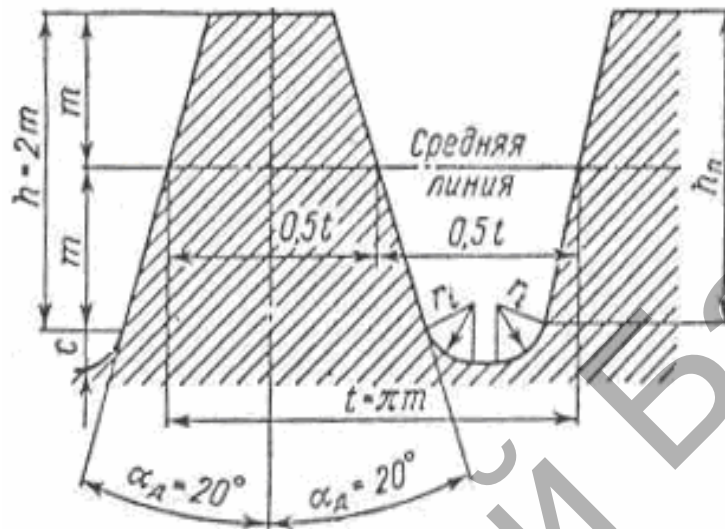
Исходный контур эвольвентной зубчатой передачи
